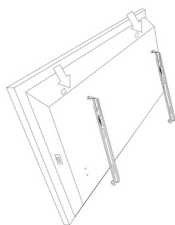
Befestigung des oberen Hakens, Hinteransicht
